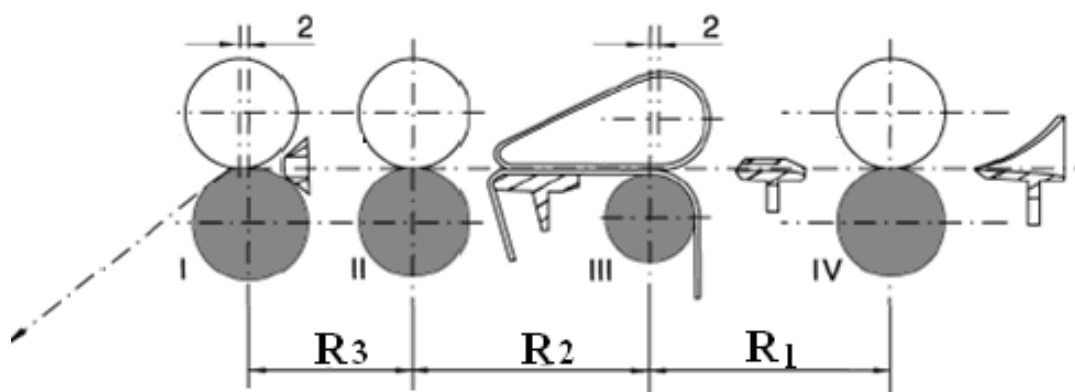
Четырехцилиндровый двухремешковый вытяжной прибор на ровничной машине ф. Zinser мод. 668
